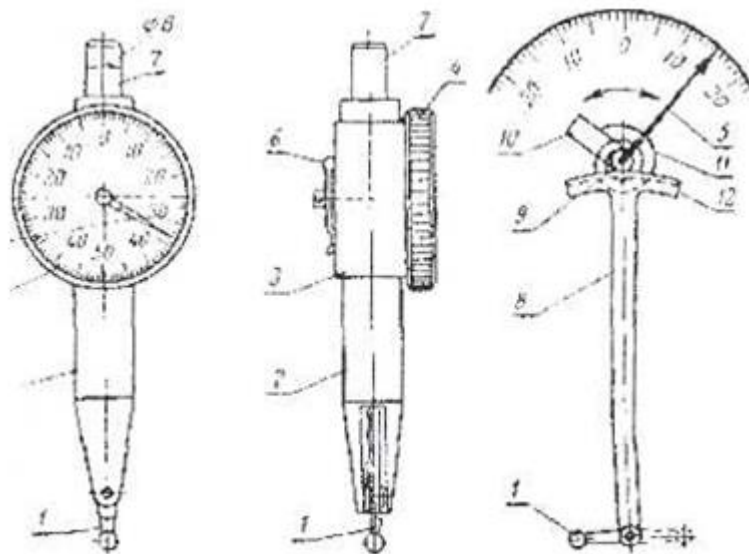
Важільно-зубчастий індикатор (а) і його принципова схема (б) 1 - вимірювальний важіль; 2 - приєднувальна втулка (гільза); 3 - корпус; 4 - обичайка; 5 - стрілка; 6 - повідок для перемикання стрілки; 7 - приєднувальний стержень; 8 - важіль; 9 - зубчасте колесо; 10 - повідок; 11 - спіральна пружина; 12 - зубчастий сектор
